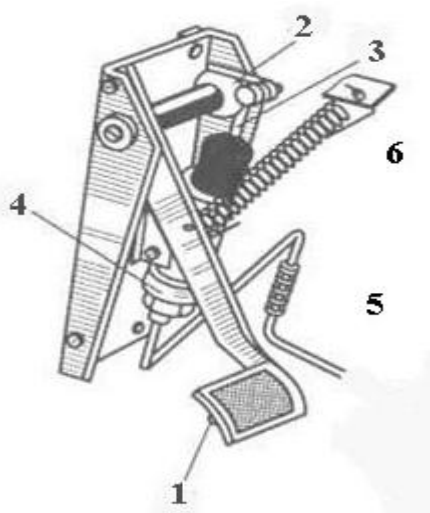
Привод выключения сцепления: 1 - педаль; 2 - рычаг; 3 - шток поршня; 4 - главный цилиндр; 5 - трубопровод; 6 - оттяжная пружина.
